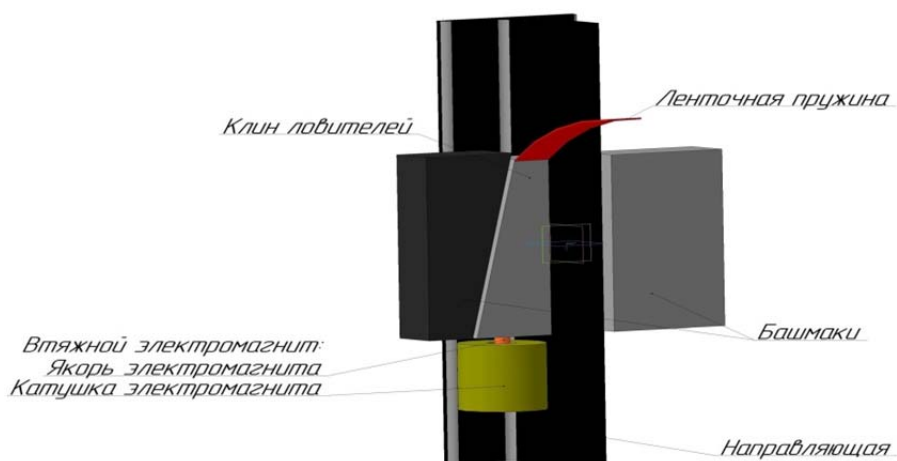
Предлагаемая схема размещения клинового ловителя.
